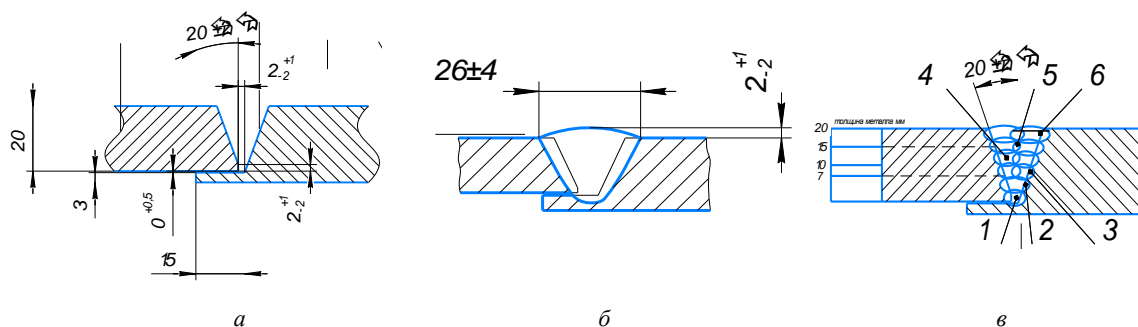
Конструктивные элементы при дуговой сварке плавящимся электродом в защитном газе:
